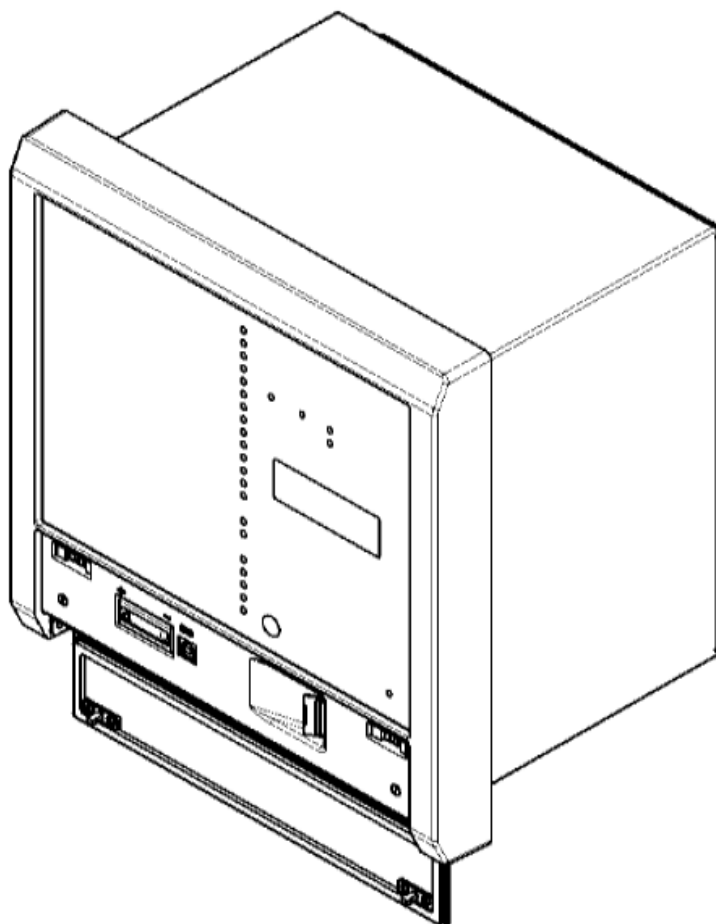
Внешний вид устройства с открытой защитной крышкой (пример)
